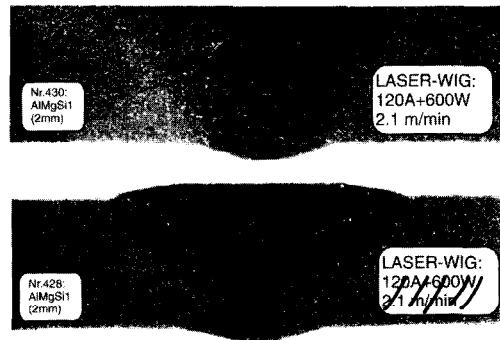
Querschnitte von Laserstrahl-WIG-Schweißnähten an 2 mm dicken AlMgSi1-Blechen.
